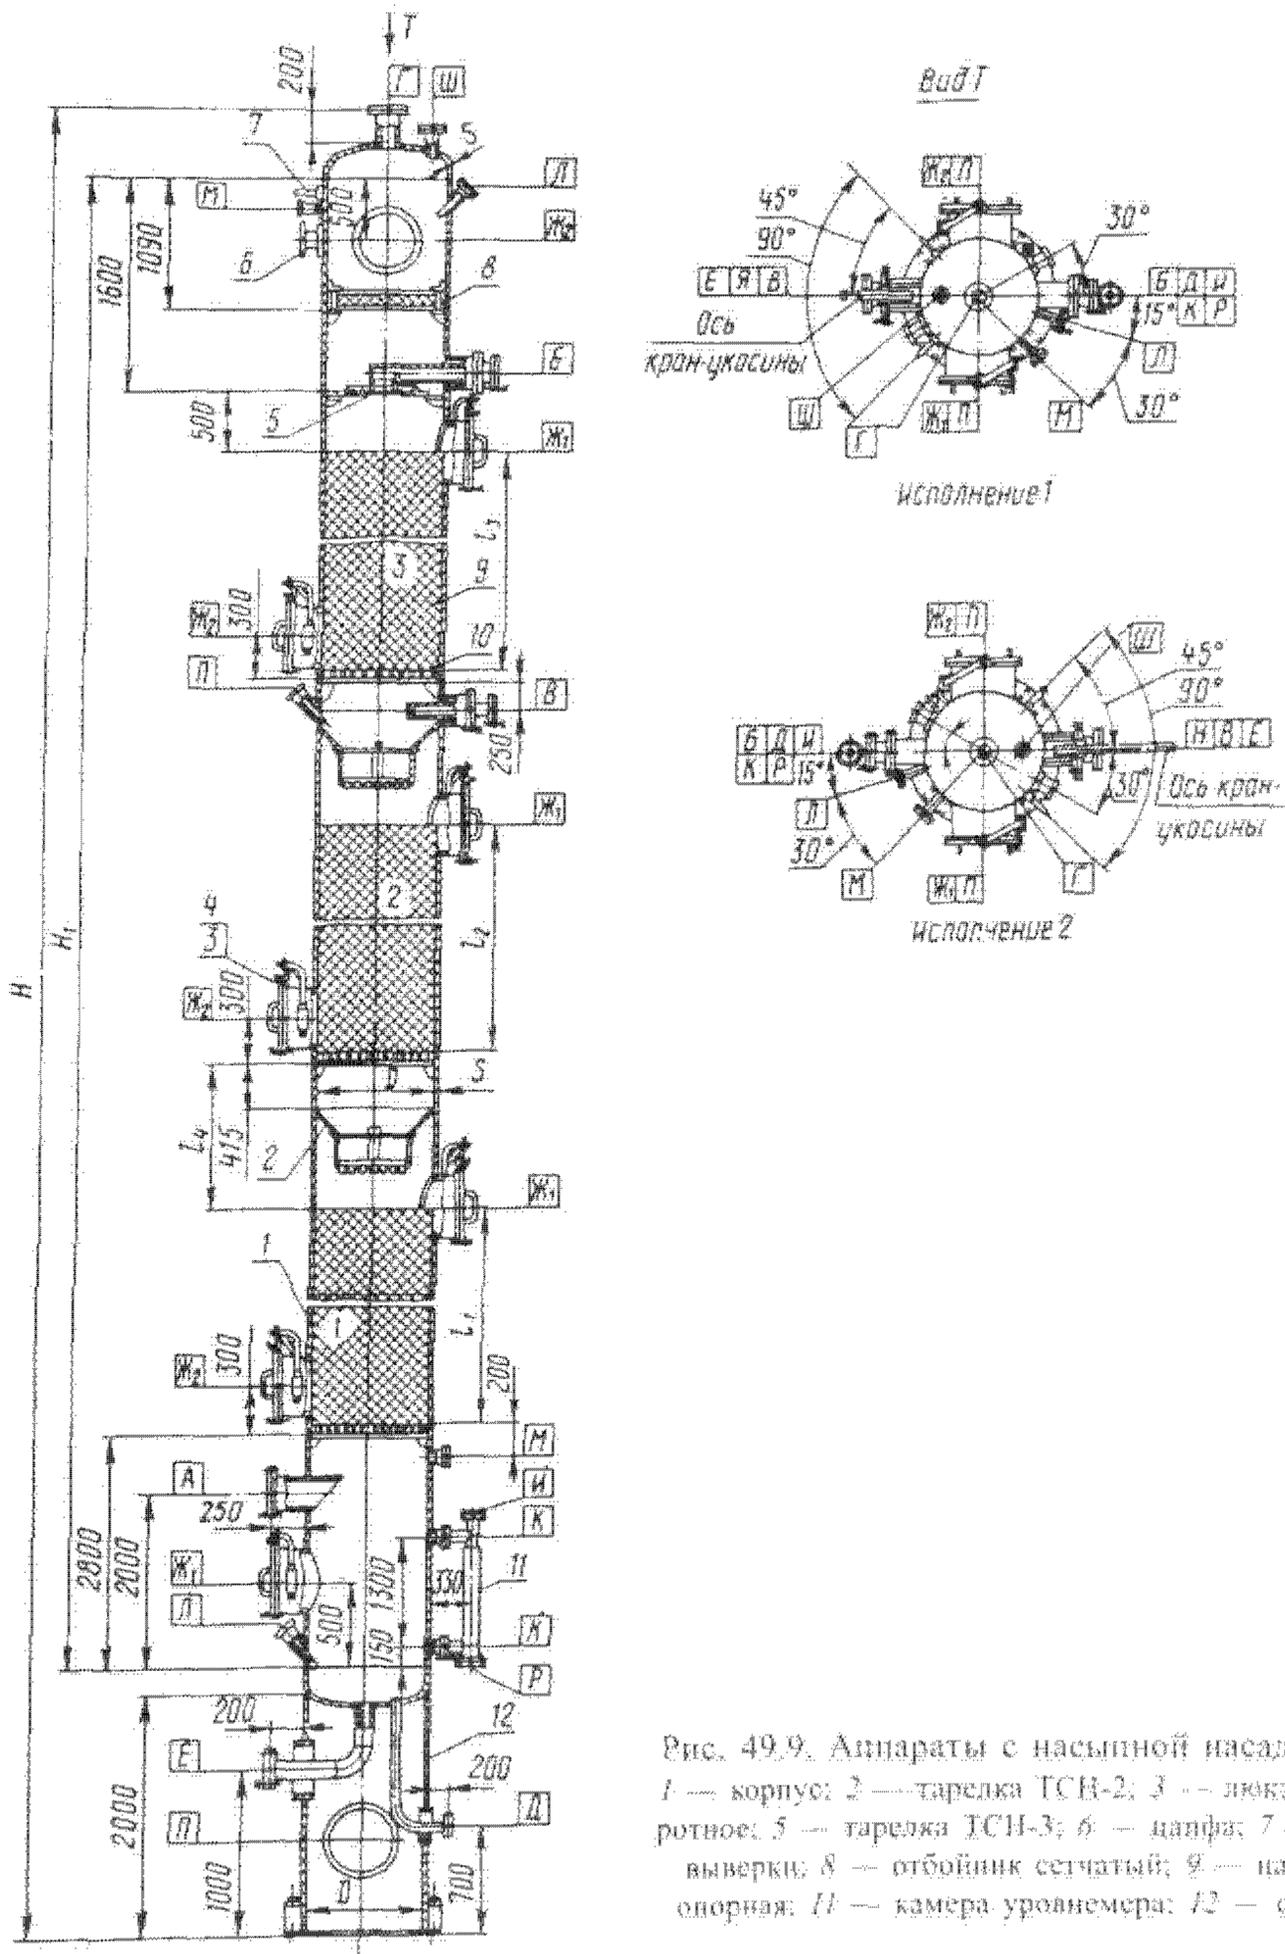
Аппараты с насыпной насадкой цельносварные: 1 — корпус; 2 — тарелка ТСН-2; 3 — люк; 4 — устройство поворотное; 5 — тарелка ТСН-3; 6 — цапфа; 7 — приспособление для выверки; 8 — отбойник сетчатый; 9 — насадка; 10 — решетка опорная; 11 — камера уровнемера; 12 — опора цилиндрическая
